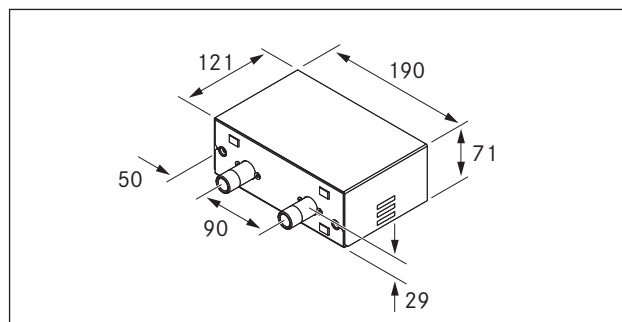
Dimensioni quadro elettrico PC32/PC3B
